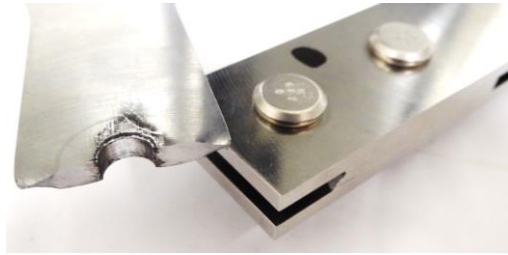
Mode de rupture des éprouvettes d'assemblage à double recouvrement.
